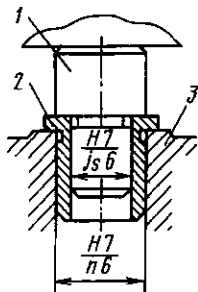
Установка опоры 1 в корпус 3 СП через переходную втулку 2
